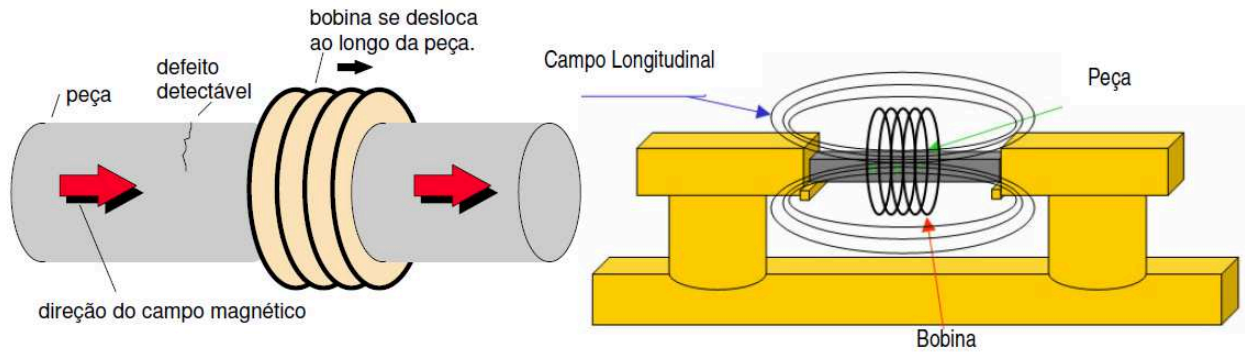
Técnica da bobina. Fonte: ABENDI 2014
